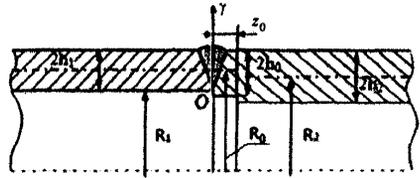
Схема стикового зварного з'єднання різновтовщинних труб
